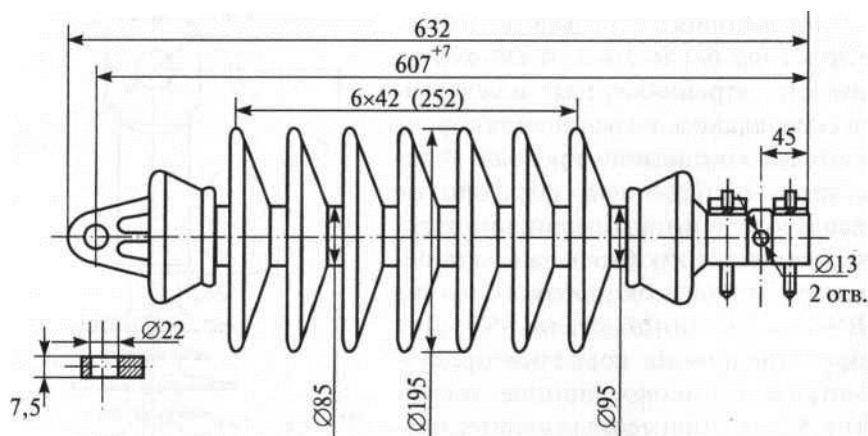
Консольный стержневой фарфоровый изолятор КСФ-70-25
